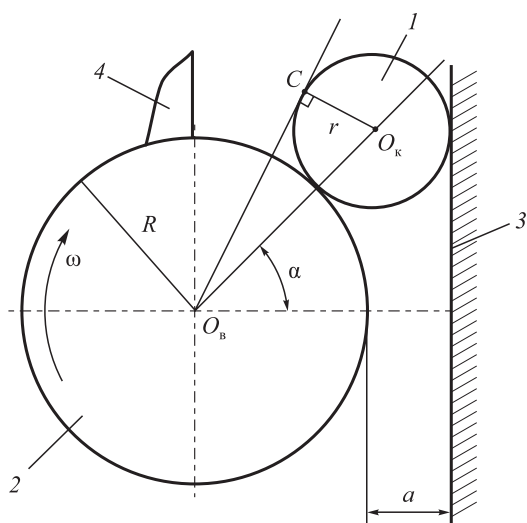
Схема одновалковой дробилки с упором на валке:
